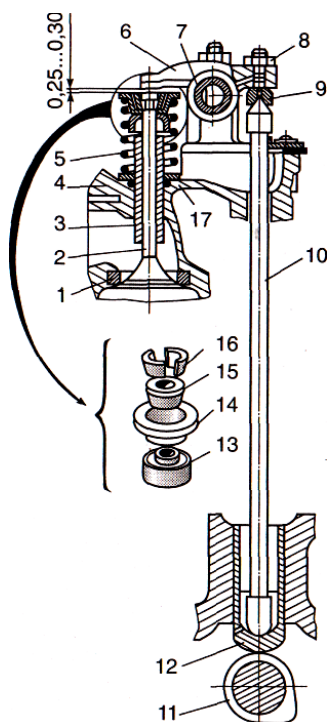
Газорозподільний механізм з нижнім розташуванням розподільного вала та верхнім - клапанів:
